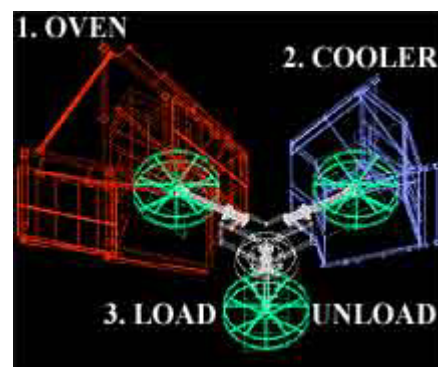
Vista en 3D de una Máquina de Rotomoldeo tipo Carrusel
